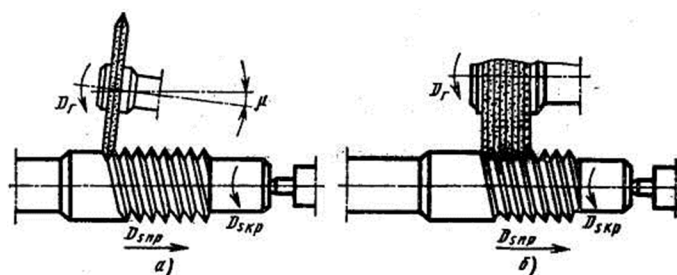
Схемы нарезания резьб на резьбошлифовальном станком кругом
